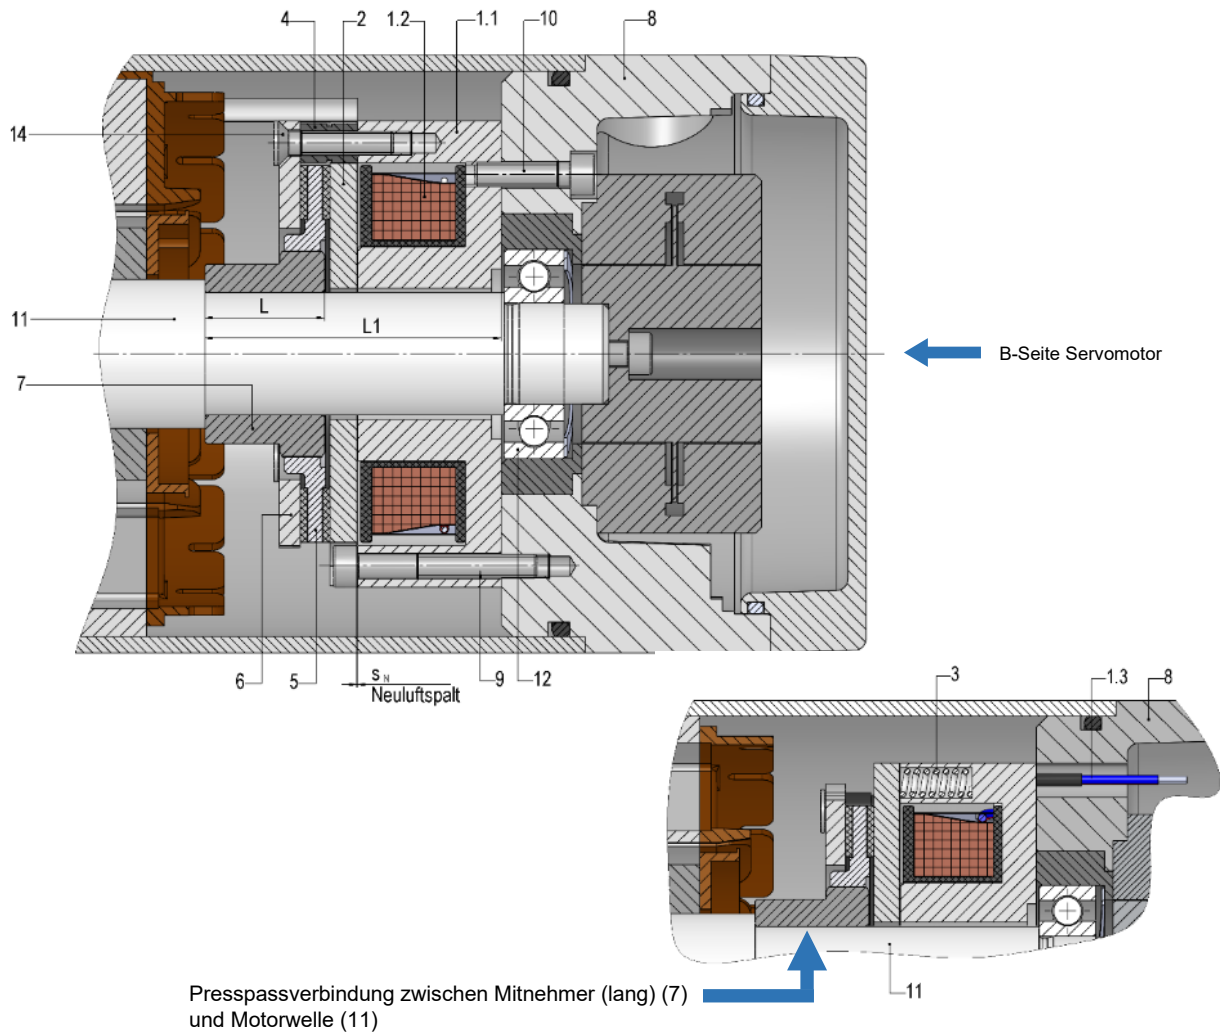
/1: Einbau der Federdruck-Einscheibenbremse KS 100..A00 und KS 10208A.. in den Servomotor, z.B. Motor B-Seite, mit Anschlag des Mitnehmers (lang) (7) an der Anschlagshulter der Motorwelle (11) und Verbindung des Mitnehmers (lang) (7) mit der Motorwelle (11) durch Presspassverbindung (Darstellung stirnseitige Befestigung (oben) und flanschseitige Befestigung (unten))
